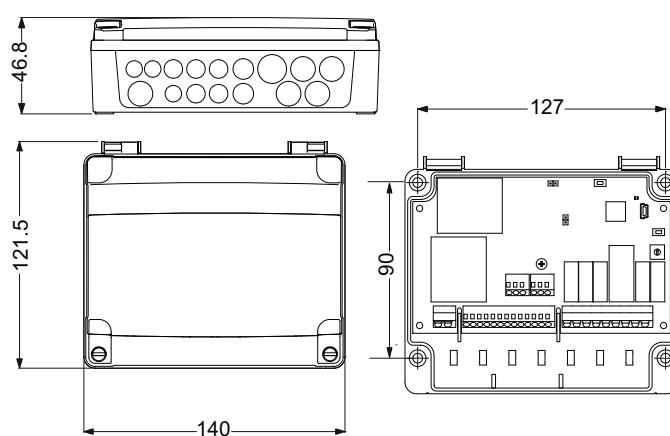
Dimensioni (mm) unità THS2-0MM.
